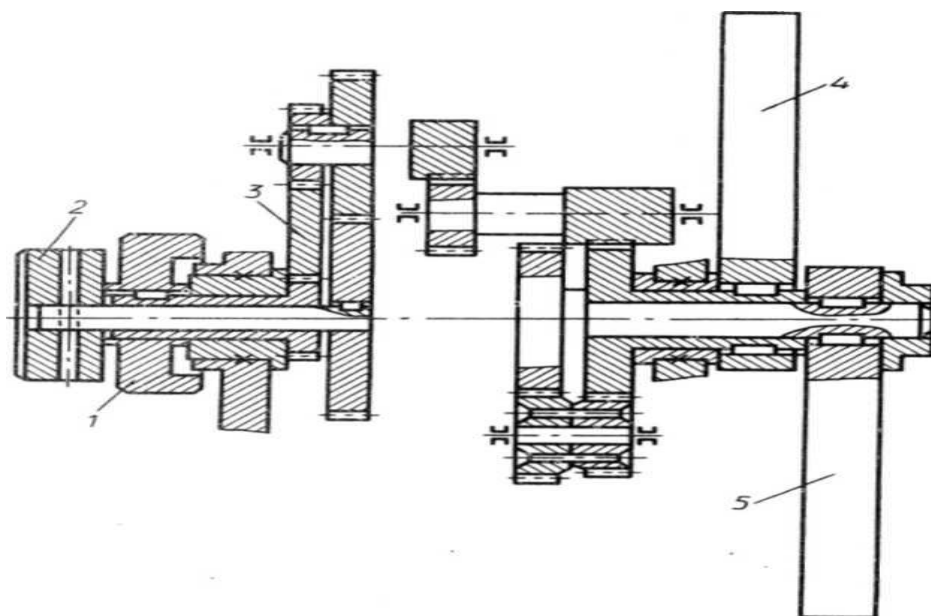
Схема балансировочного механизма ЭНИМС для автоматического уравнивания круга на шлифовальном станке
